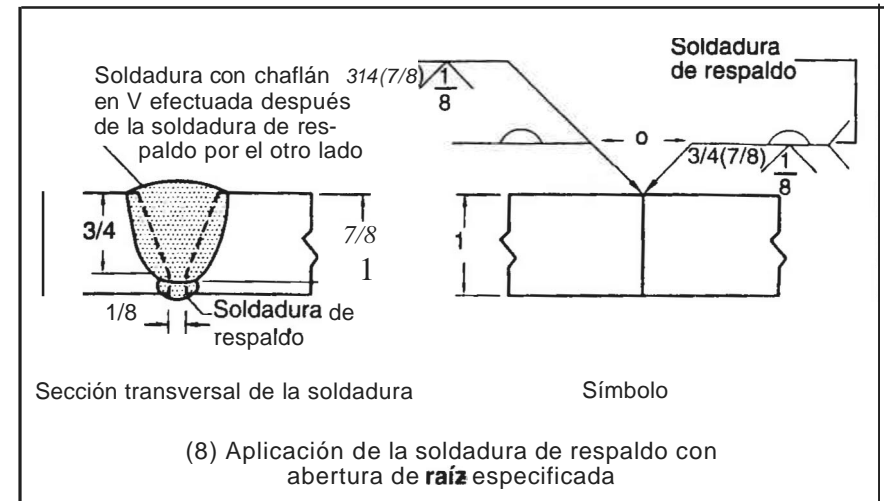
(CONTINUACIÓN): APLICACIONES DEL SÍMBOLO DE SOLDADURA DE REVERSO O RESPALDO
